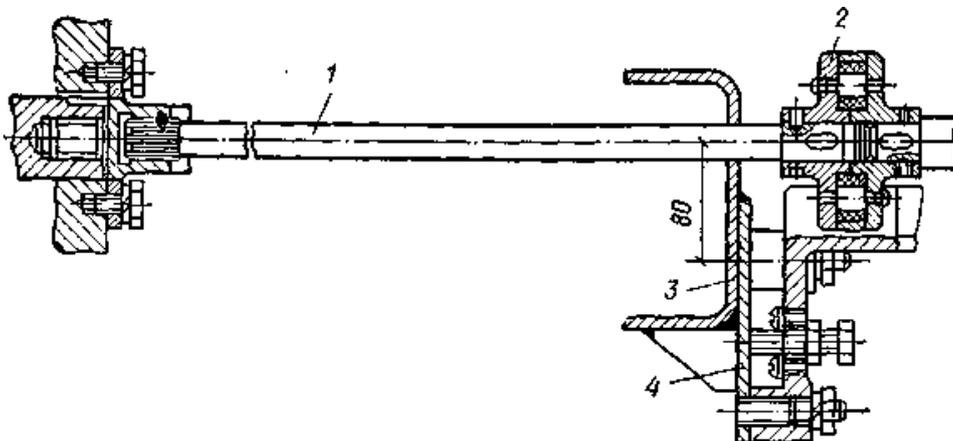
Установка насоса НШН–600 на шасси автомобилей ЗИЛ: 1 – вал привода; 2 – муфта; 3 – бампер; 4 – косынка
